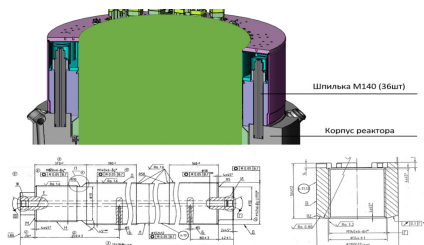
Общий вид фланцевого разъёма корпуса реактора.
